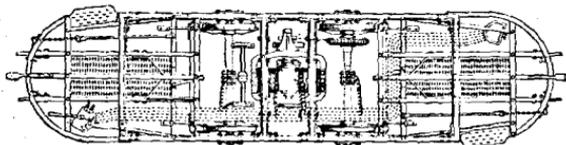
Vue en plan du Tramway de M. Holroyd Smith.
